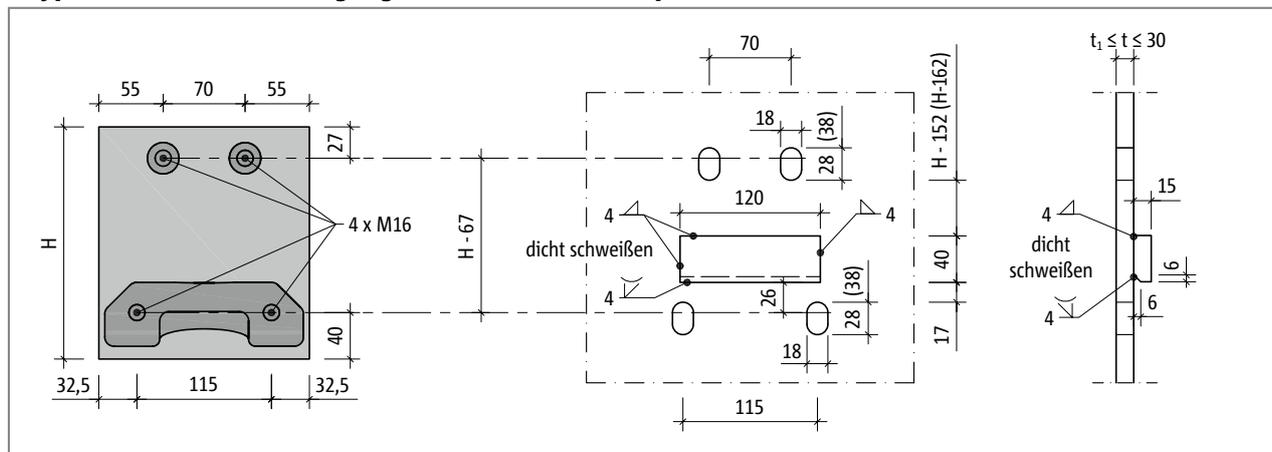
Schöck Isokorb® T Typ SK-M1: Konstruktion des Stirnplattenanschlusses
